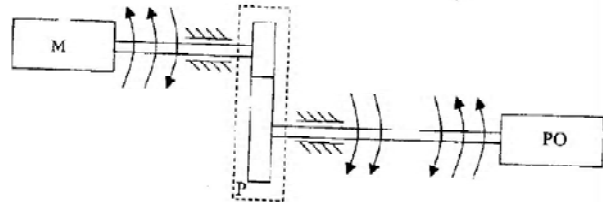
Кінематична схема з пружним валом: М – двигун, РО – робочий орган механізму, Р – редуктор
